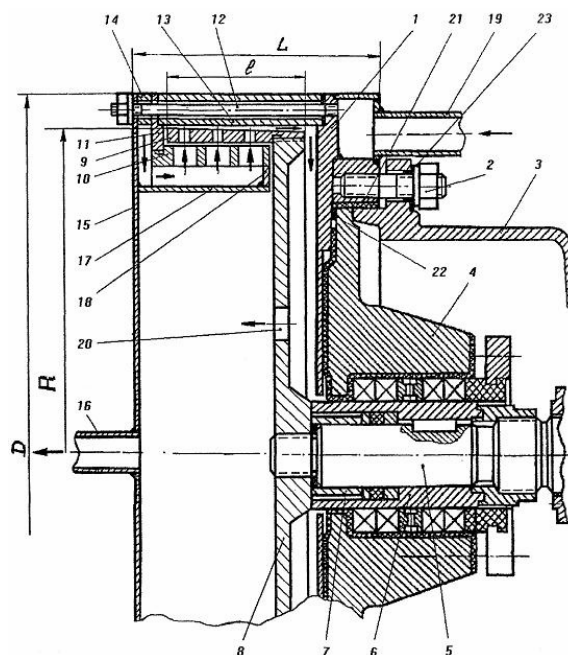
Роторний пристрій сиренного типу [24]: 1 – опорний вузол; 2, 12 – шпилька; 3 – корпус; 4 – чепцевий вузол; 5 – вал; 6 – змінний кільце; 7 – чоп; 8 – рухомий диск; 9 – рухома каблучка; 10 – нерухома каблучка; 11 – нерухомий диск; 13 – обод; 14 – проміжна каблучка; 15 – днище; 16 – штуцер; 17 – каблучка-перегородка; 18 – шайба; 19 – патрубок підводу рідини; 20 – отвори; 21 – теплоізолююча каблучка; 22 – прокладка; 23 – теплоізолююча шайба
